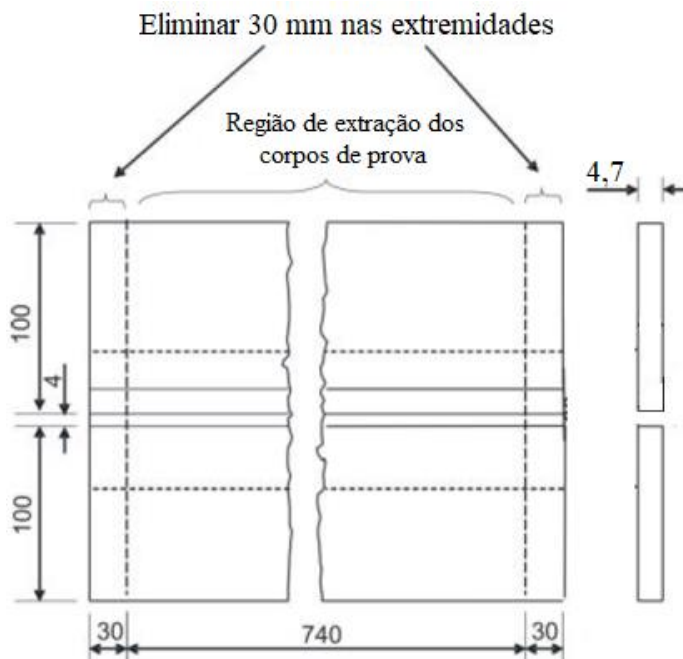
Representação esquemática da junta de solda (dimensões em mm).
